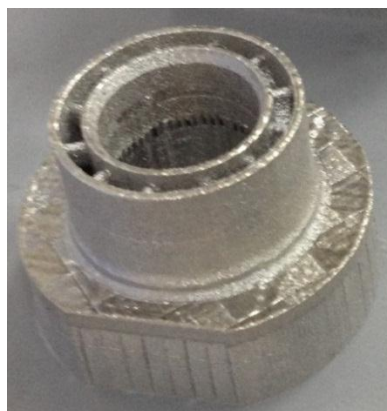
Внешний вид выращенной заготовки завихрителя ФГУП «ВИАМ»
